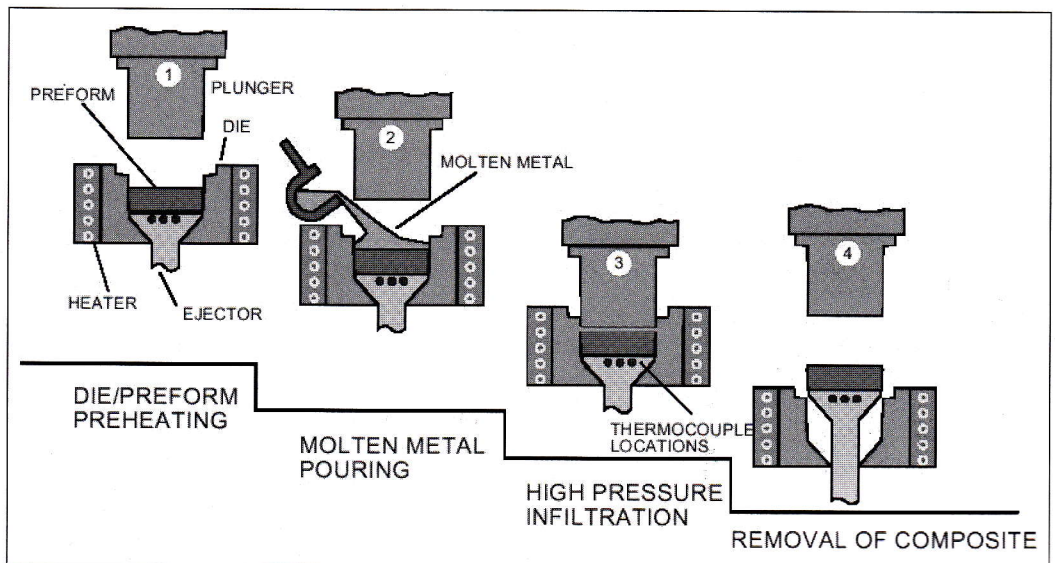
Schematizzazione del processo di Squeeze Casting diretto [15].
